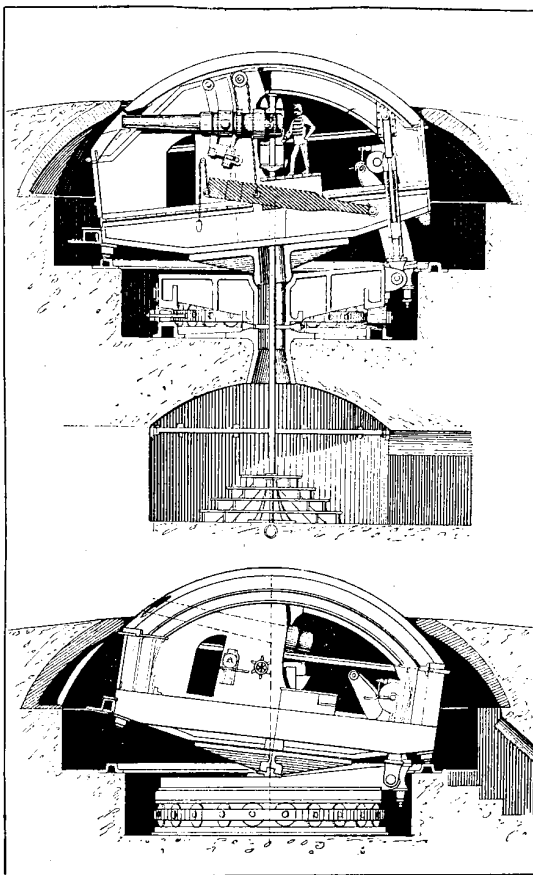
Tourelle oscillante Mougin (page 149, col. 2).
